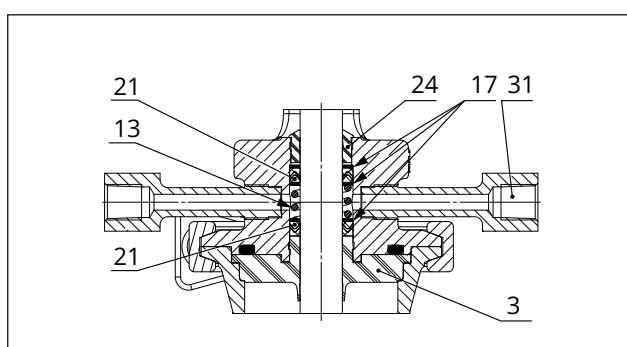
DN 15...80 · Exécution moulée avec joint de tige en PTFE et barrière vapeur
